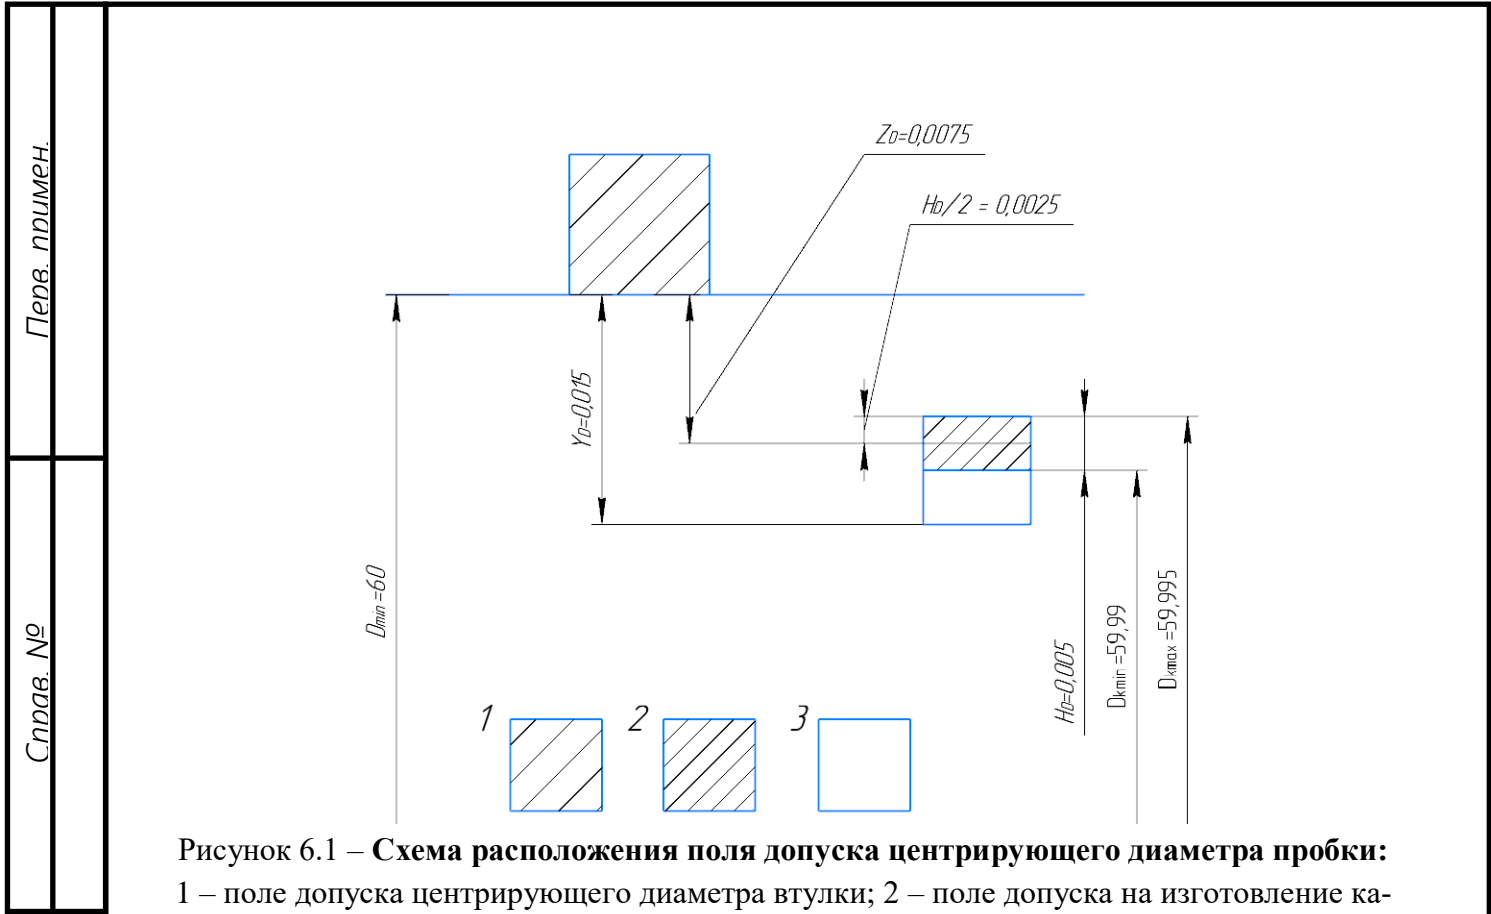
Схема расположения поля допуска центрирующего диаметра пробки:
